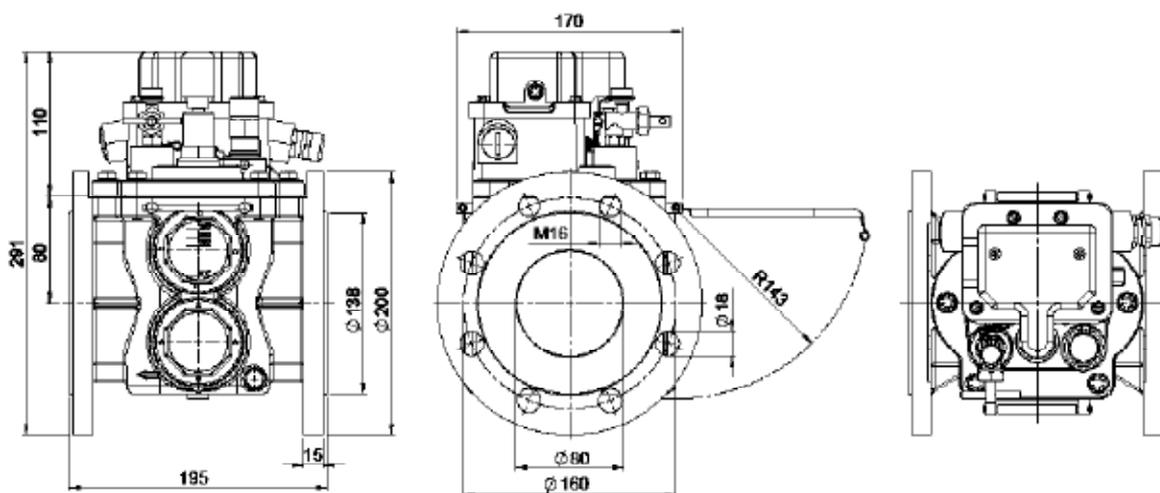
Размерный эскиз газового реле типорядаNM типа 26 (BF 80/10/8)
